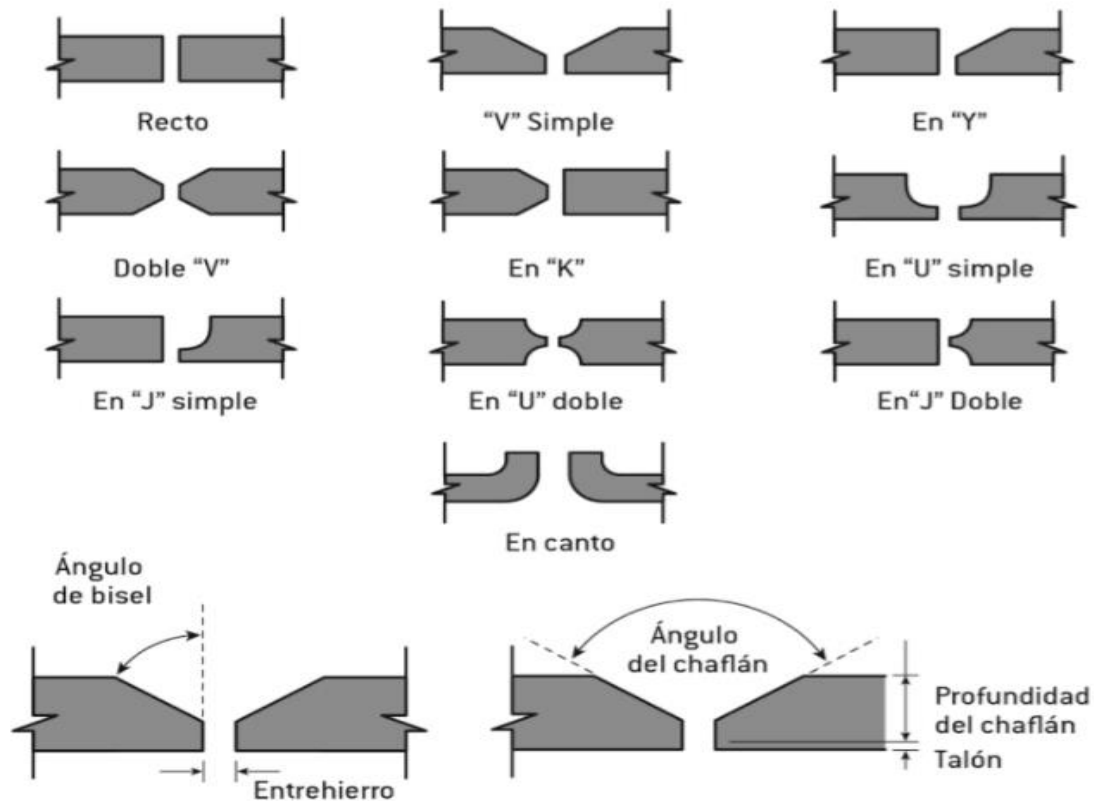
Preparación de soldes. Interpretación de soldadura UF1640
